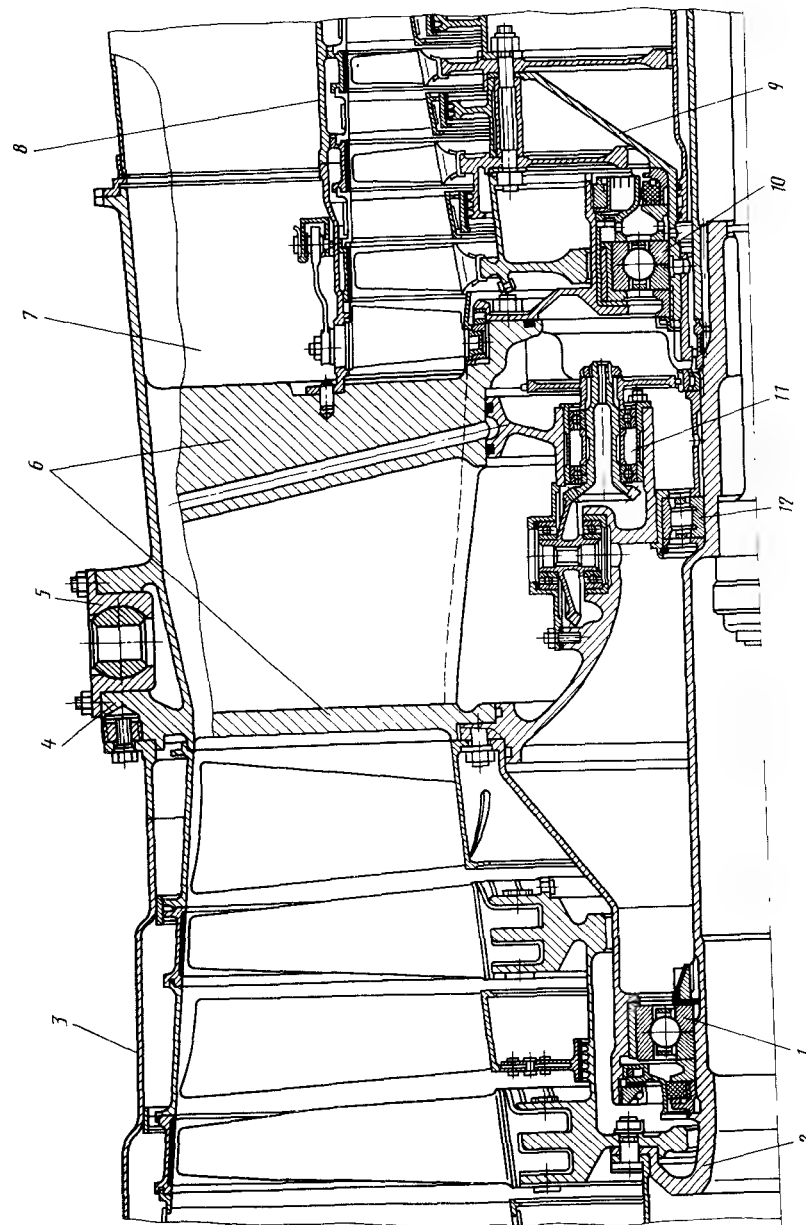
Силовой разделительный корпус двухкаскадного компрессора ТРДД АИ-25
